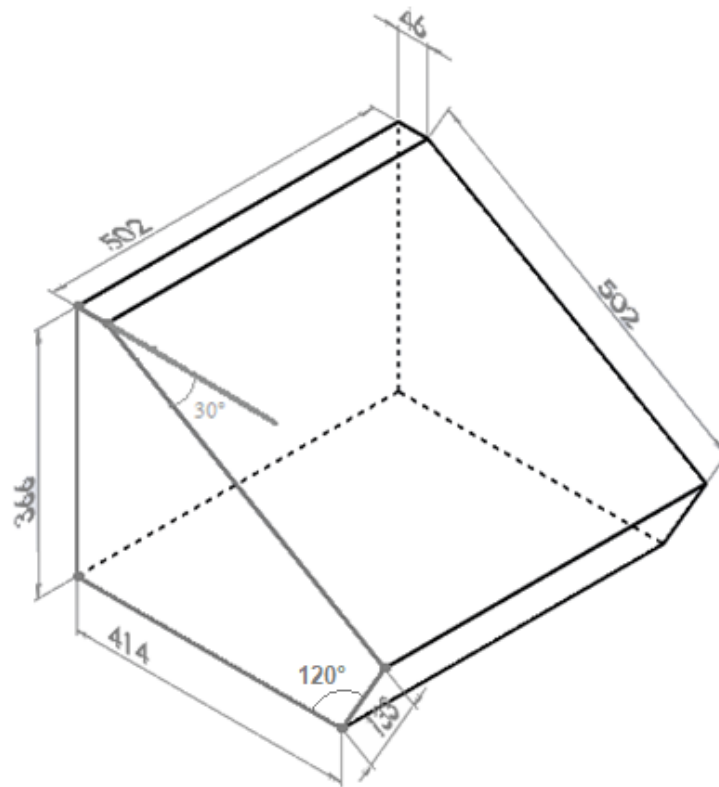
dimensions (en millimètre) du four solaire type boîte
